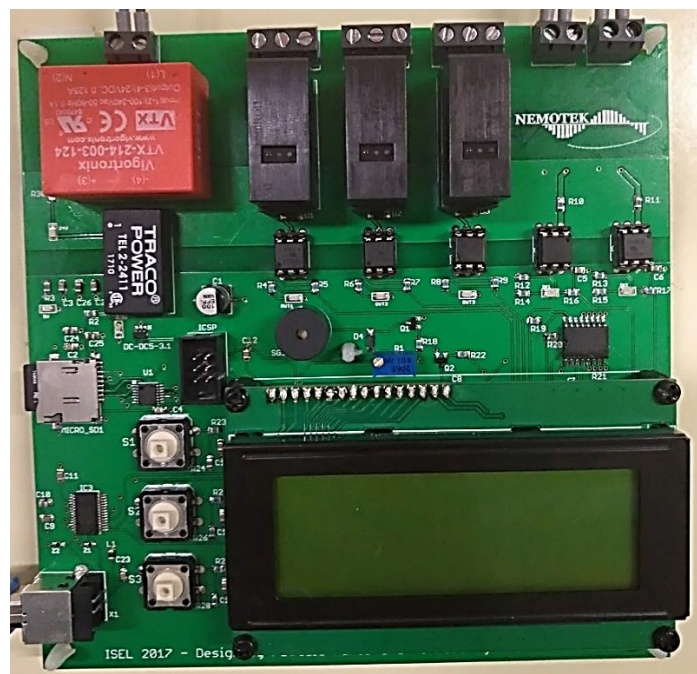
Aspeto do PCB com os componentes inseridos, com o LCD colocado (placa eletrónica).
